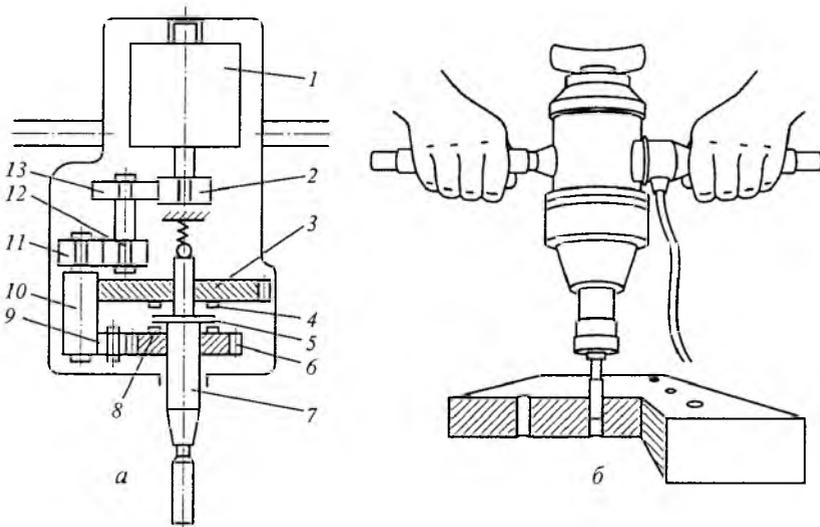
Резьбонарезатель с электрическим приводом:
